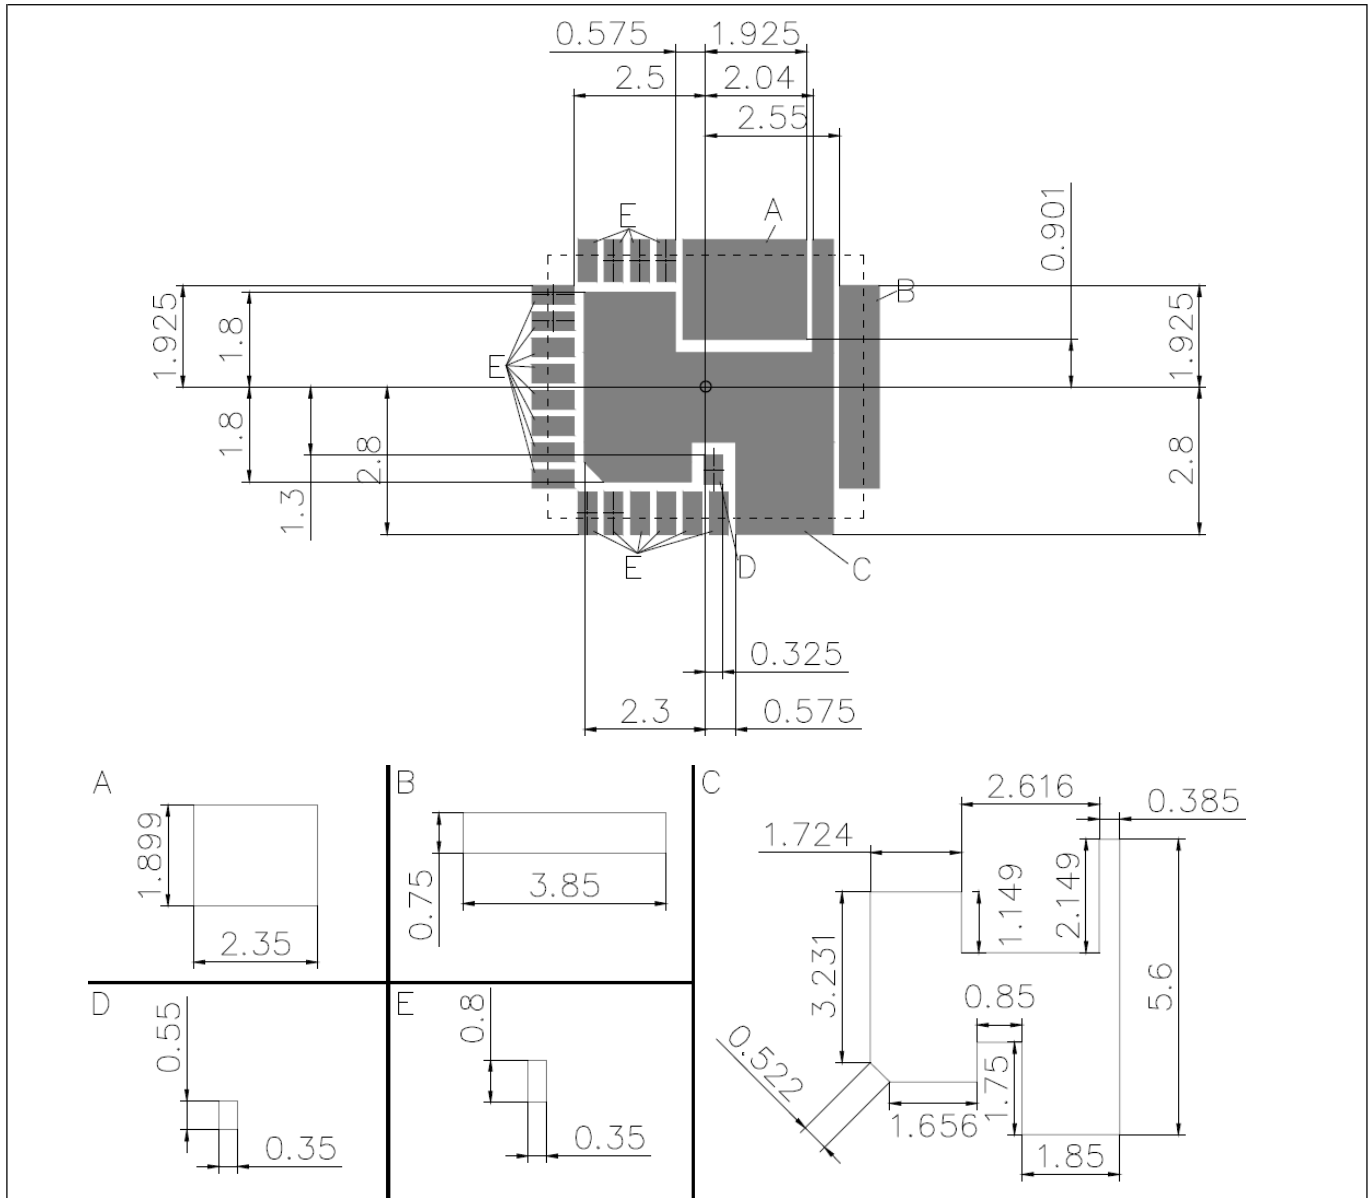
PCB 金属焊盘尺寸和间距（所有尺寸均以毫米为单位）
